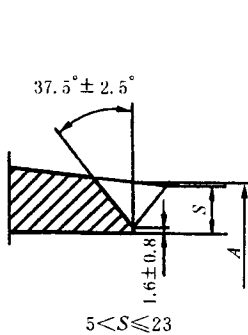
大直径对焊法兰与钢管连接的焊接接头
